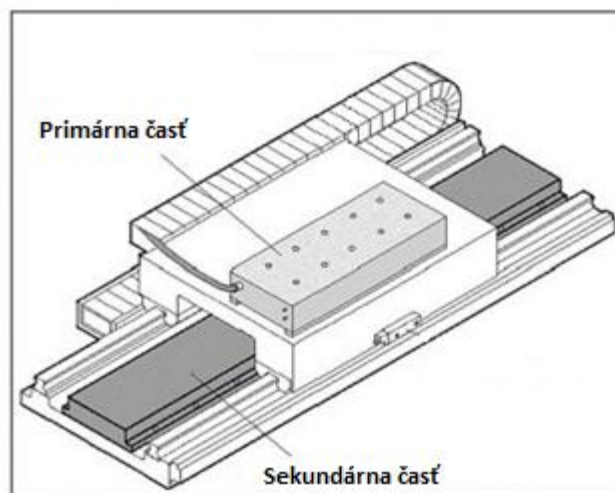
Princiálne konštrukčné usporiadanie lineárneho motora, [www.vues.cz](http://www.vues.cz)
